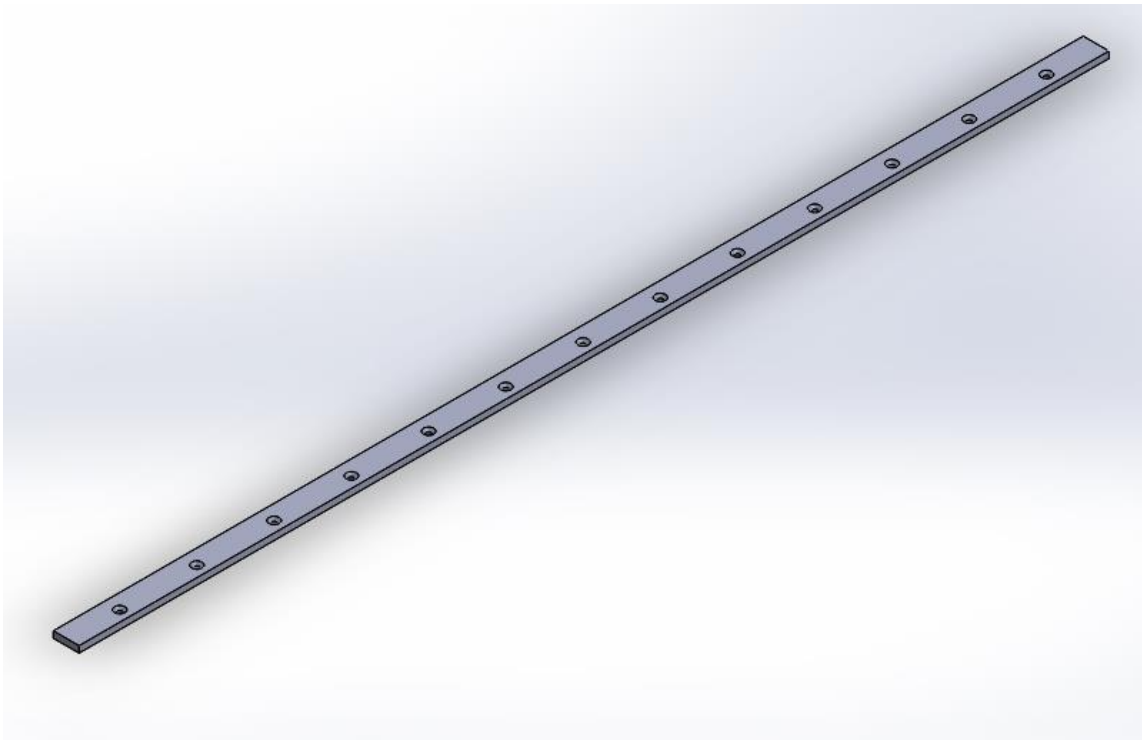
Spojna ploča - vanjske dimenzije i CAD model
